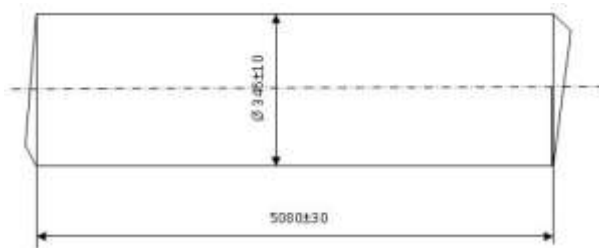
Эскиз поковки для детали «Дорн 12»
